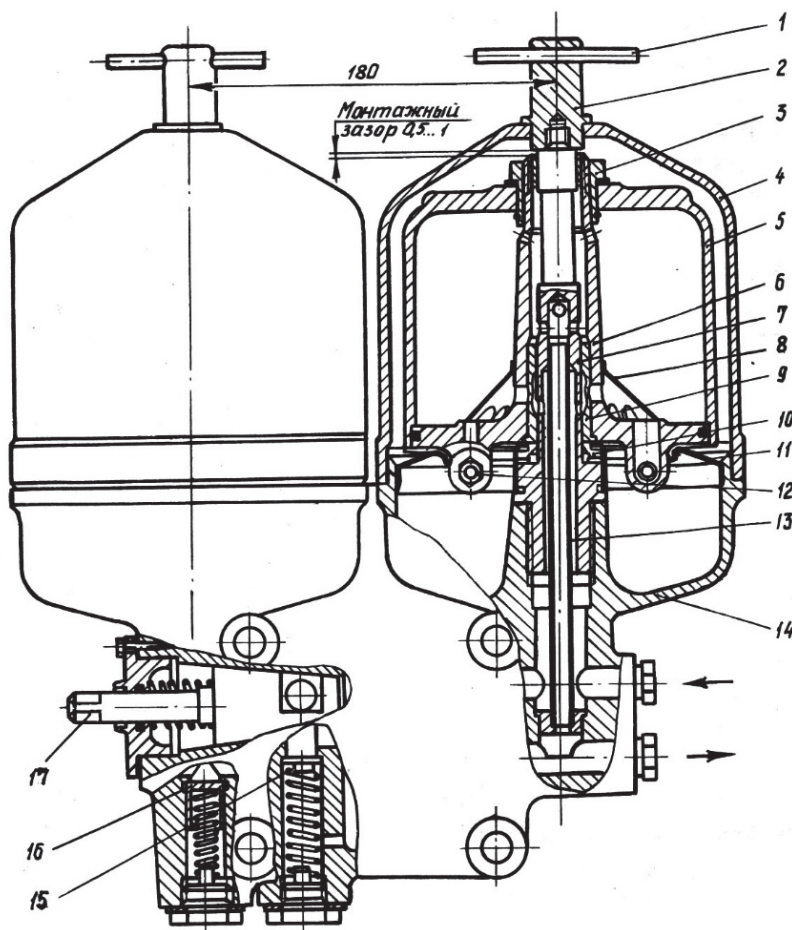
Двухроторный полнопоточный масляный очиститель 2МЦН-5П:
